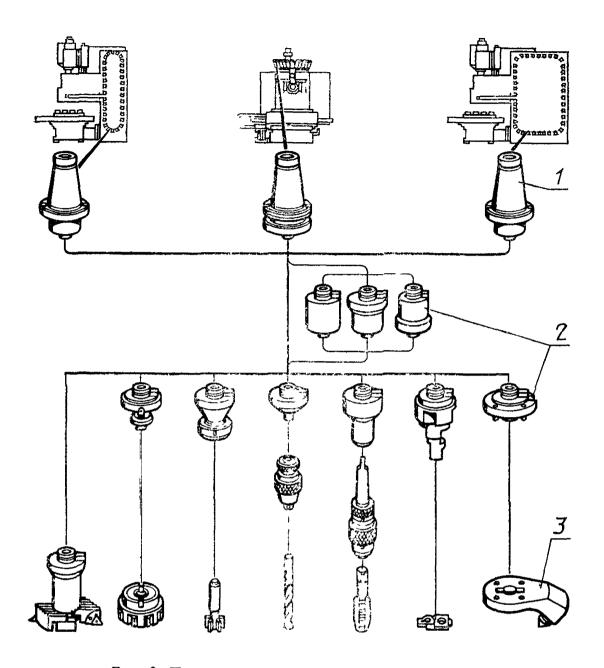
Пример блочно-модульного построения ЦКИ для станков фрезерной группы:
